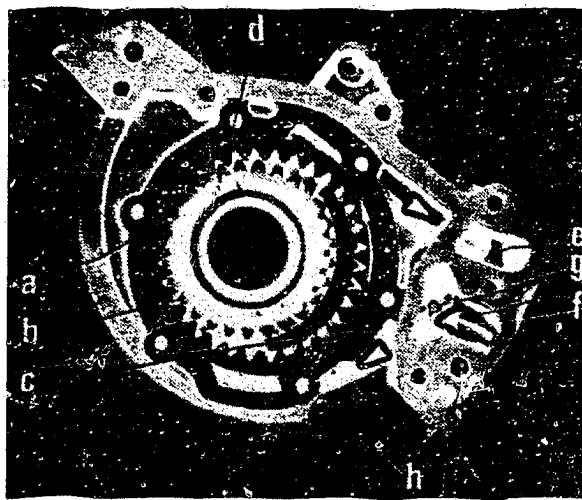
Die Sichelölpumpe mit a Aussenrad – b Innenrad – c Sichel – d Mitnehmer – e Druckseite – f Saugseite – g zum Überdruckventil – h Dichtung
